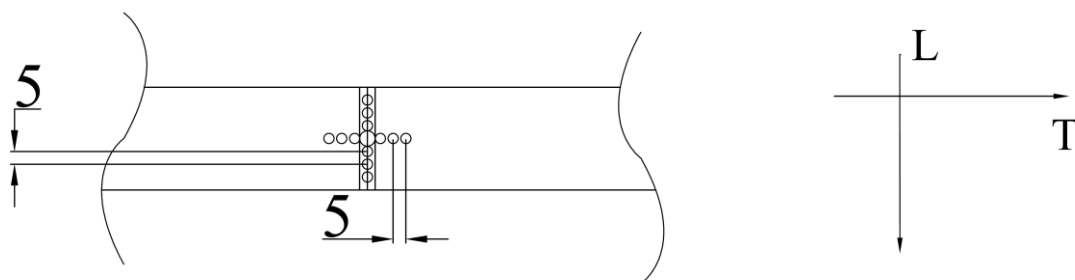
Pontos de medição dos perfis (L) longitudinal e (T) transversal (unidades em mm).
